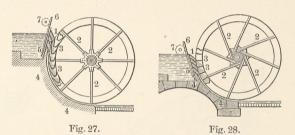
Rückenschlächtiges, Fig. 28. Mittelschlächtiges Wasserrad mit Kulisseneinlauf.
